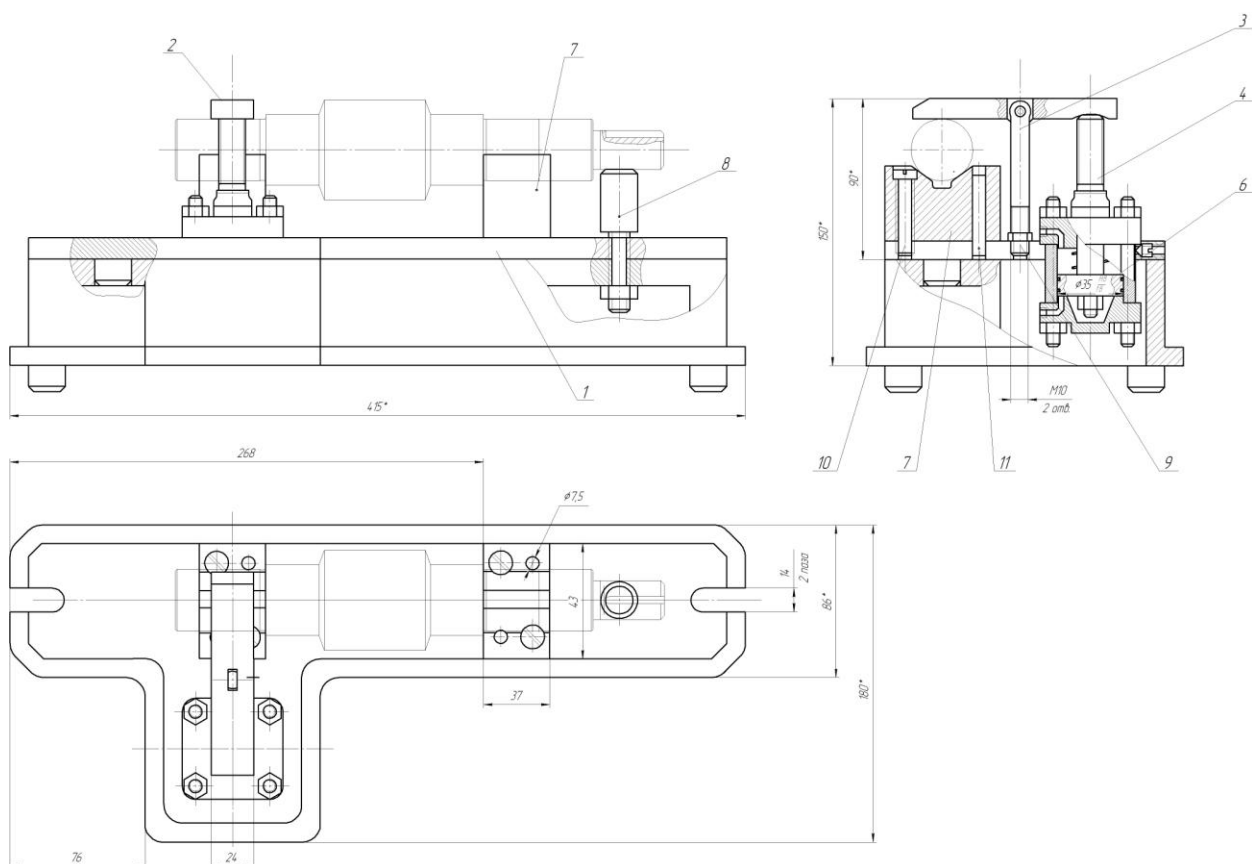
Приспособление для шпоночно-фрезерной операции
